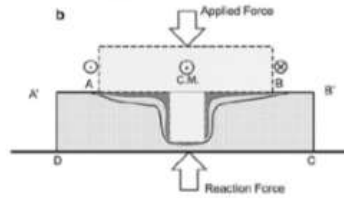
Sección transversal de la herramienta de soldadura por fricción y la pieza de trabajo
